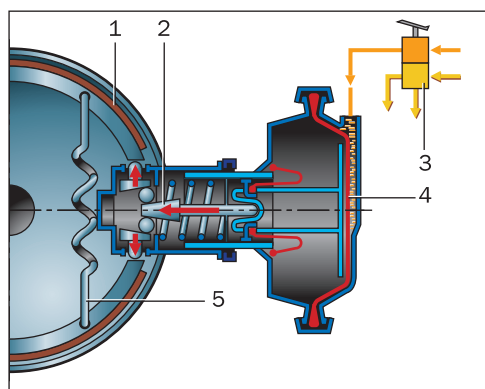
Тормозной механизм с клиновым разжимным устройством и автоматической регулировкой зазора: 1 — колодка; 2 — разжимной клин; 3 — тормозной кран; 4 — тормозная камера; 5 — пружина
